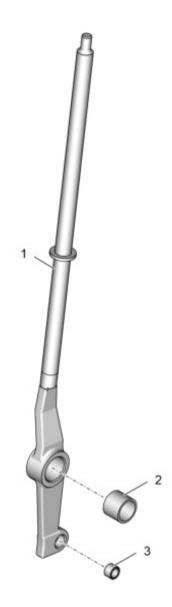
4320-1804037 Рычаг блокировки дифференциала раздаточной коробки с втулками
